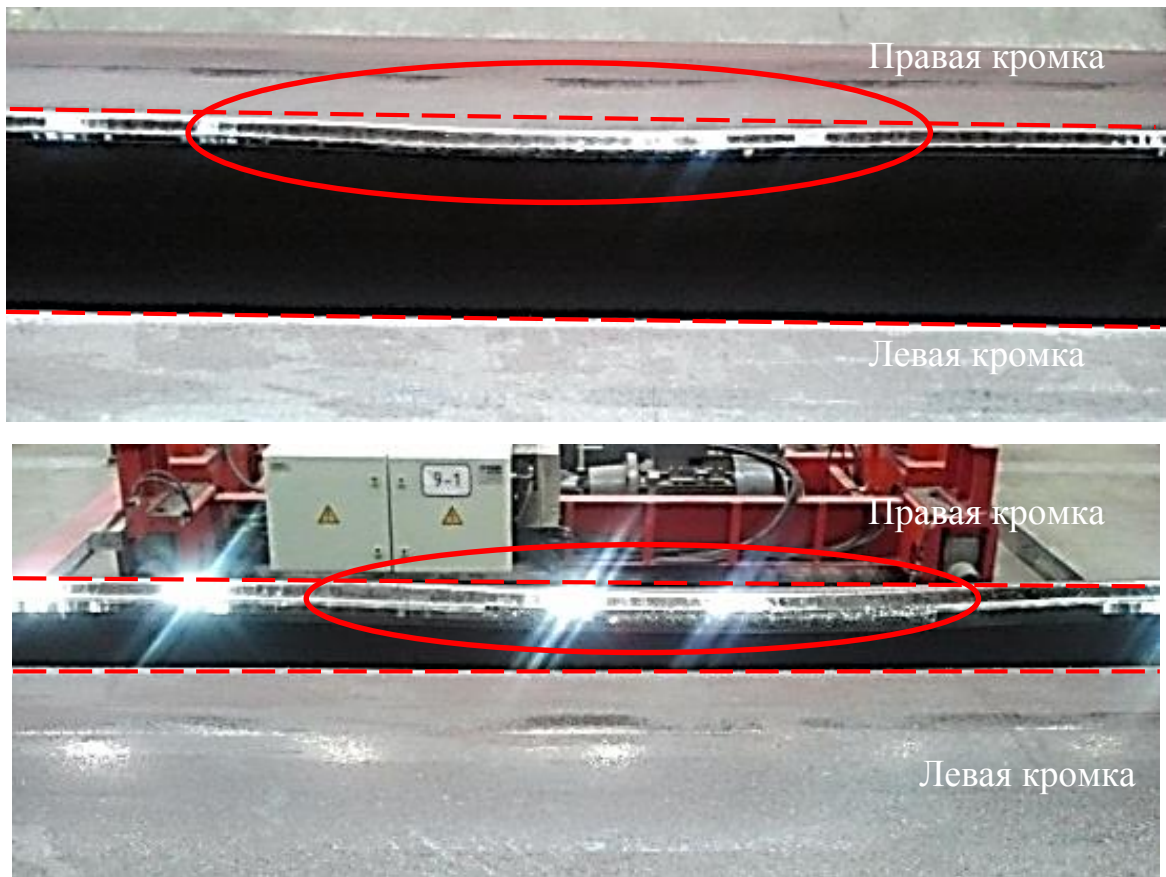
Продольный вид кромок сформованной трубной заготовки
